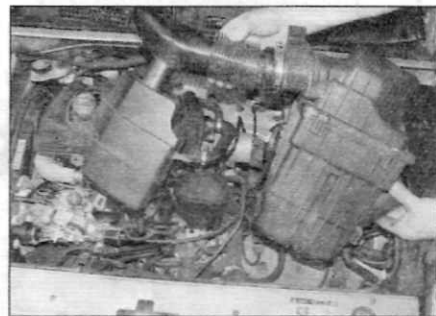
Извлеките корпус воздушного фильтра и воздухопровод из моторного отделения как единый элемент (поздние модели с двигателем 1.9 л)
